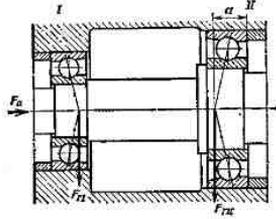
Схема установки радиально-упорных подшипников в ступице колеса
